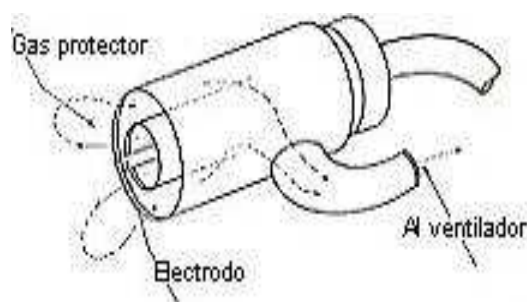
Extracción incorporada a la pistola de soldadura.
